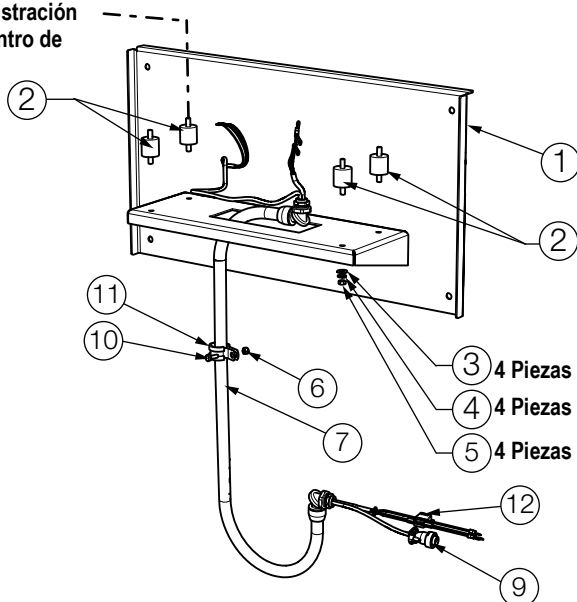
Ilustración de las piezas del conjunto de montaje y cableado del centro de pesaje
